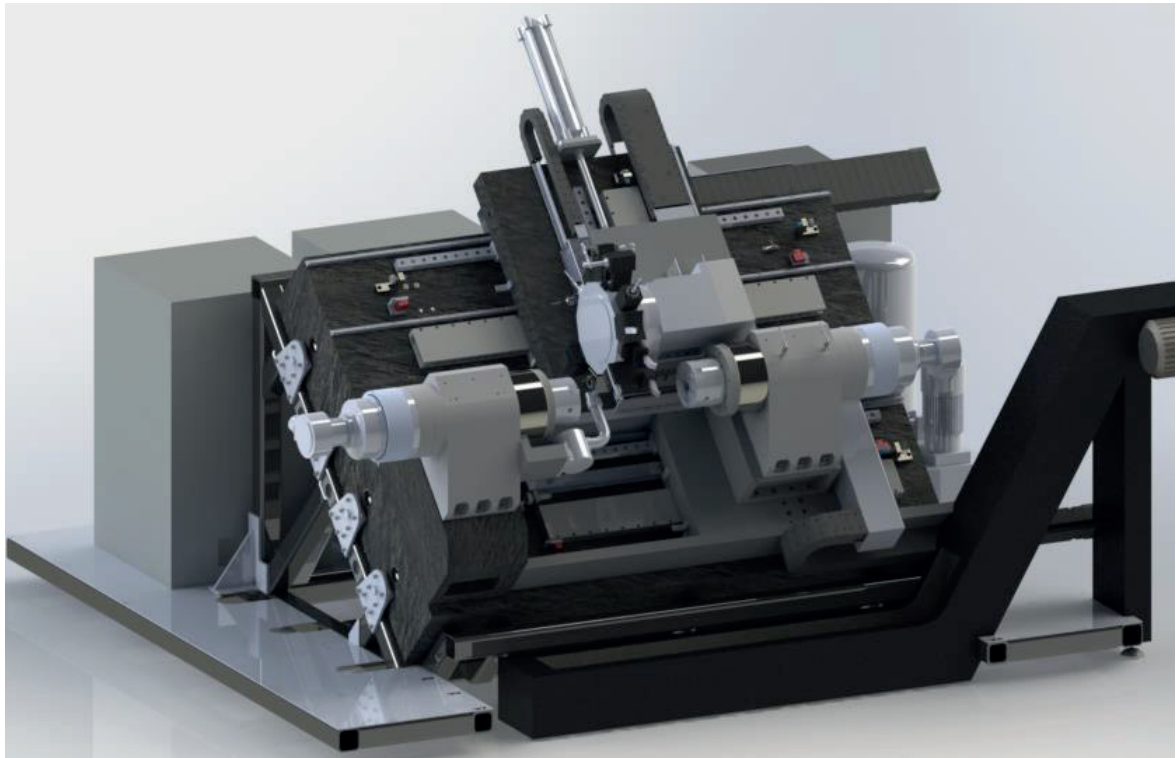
Вид высокоточного токарного обрабатывающего центра с ЧПУ модели «ТМ-160» без кабинетного ограждения
